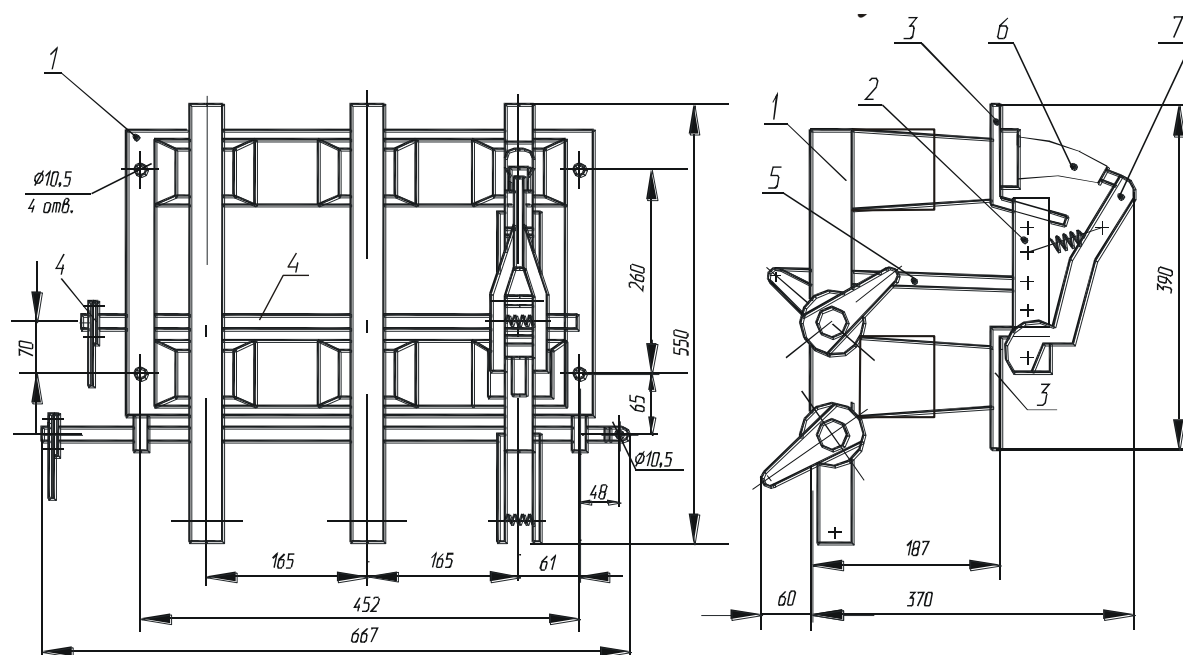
Выключатель нагрузки ВНМ-10 с ножами заземления снизу
